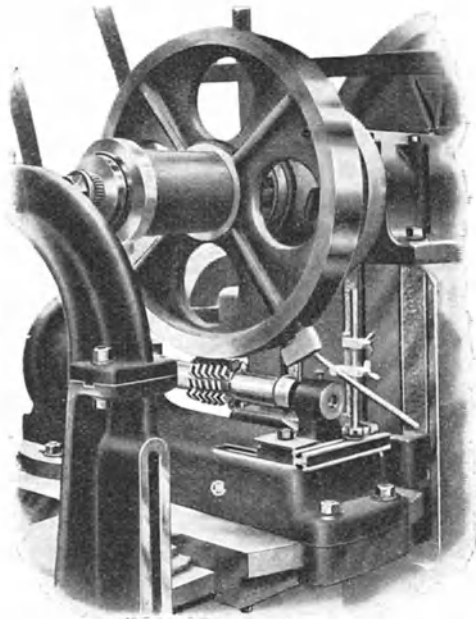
Stirnradfräsmaschine nach dem Abwälzverfahren von J. E. Reinecker.
